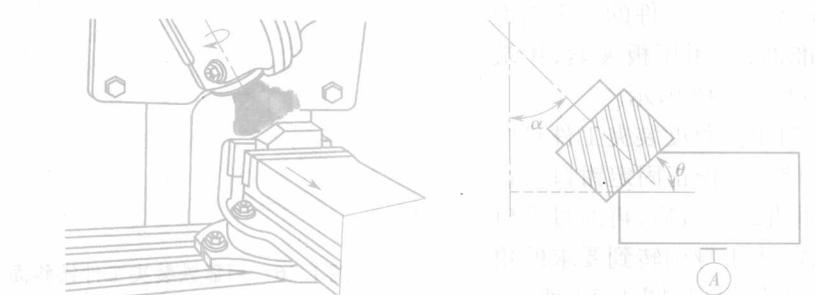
工件定位基准面与工作台台面平行安装用端铣刀铣斜面
